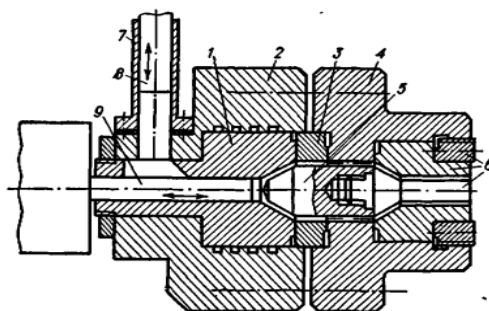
Схема пластикатора: 1 – цилиндр, 2 – корпус, 3 – кольцо, 4 – головка, 5 – торпеда, 6 – мундштук, 7 – цилиндр, 8 – поршень, 9 – поршень.
